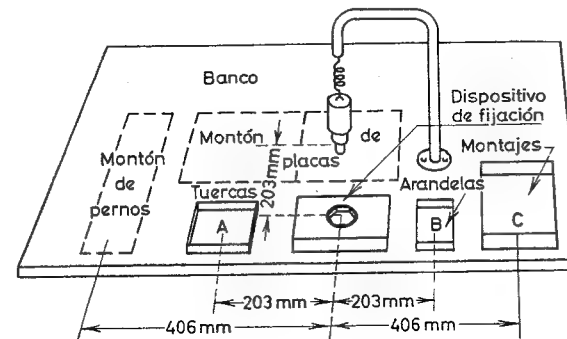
Disposición del lugar de trabajo para el montaje de placas.
